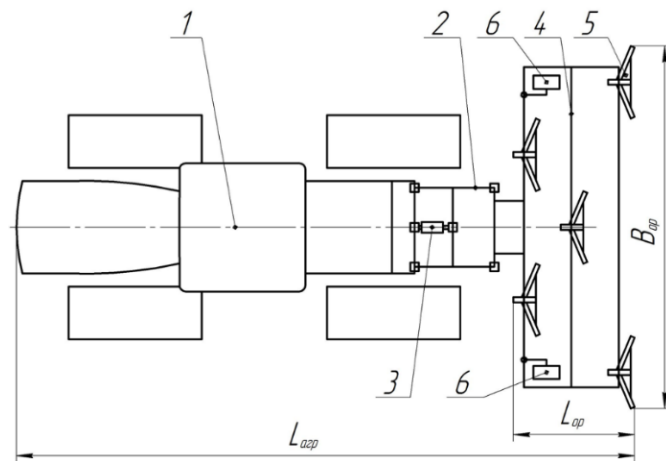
Принципиальная схема пахотного агрегата, комплектуемого плоскорезом-глубококорыхлителем ПГ-3-5: 1 – трактор; 2 – навеска; 3 – гидроцилиндр; 4 – рама орудия; 5 – рабочий орган; 6 – опорные колеса.
